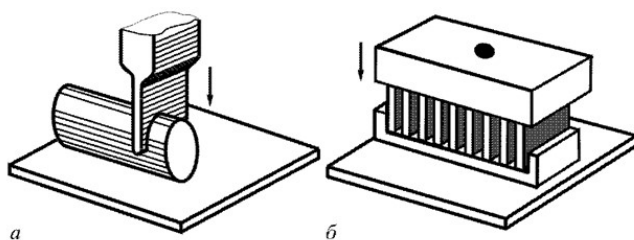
Схемы ультразвукового разрезания заготовок:
